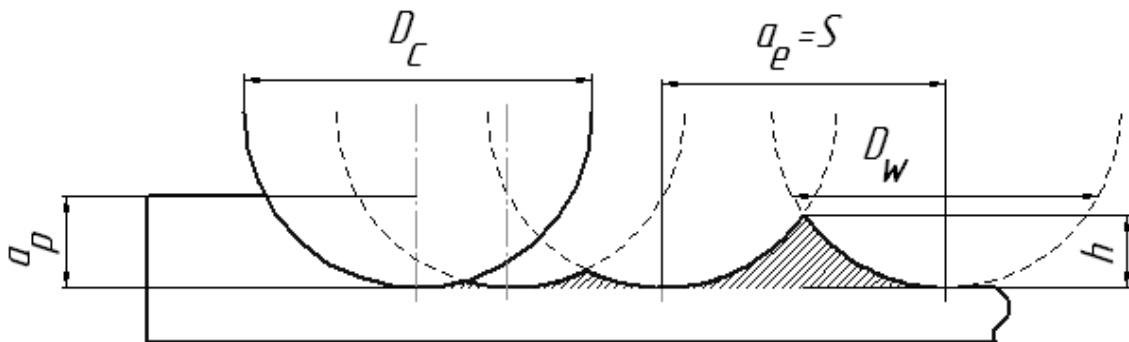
Влияние расстояния между строками на теоретическую шероховатость при построчном фрезеровании плоской поверхности: D_c – диаметр фрезы, a_p – глубина резания (мм), $a_e = S$ – ширина резания (мм), D_w – рабочий диаметр фрезы (мм), h – высота «ребешка»
